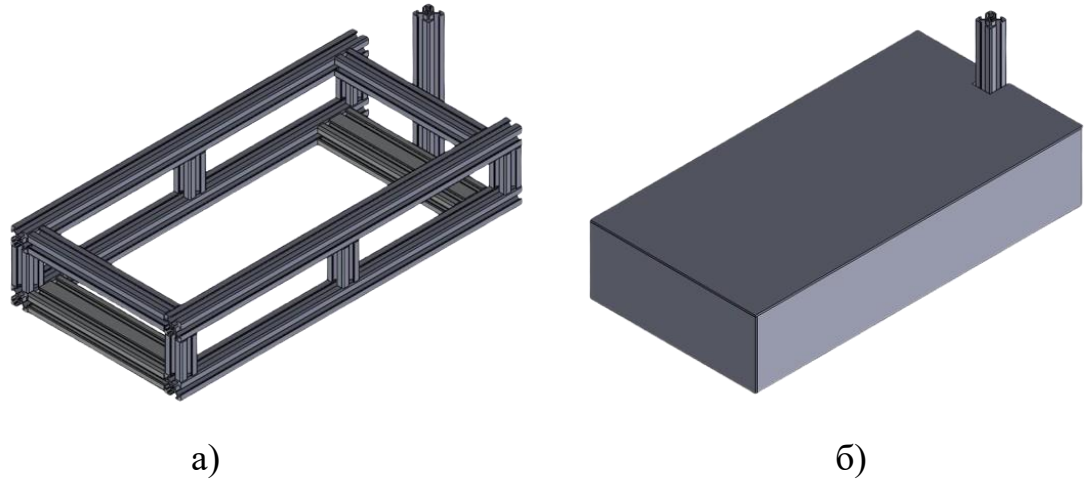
Модель рами пристрою: а) без обшивки; б) з обшивкою
